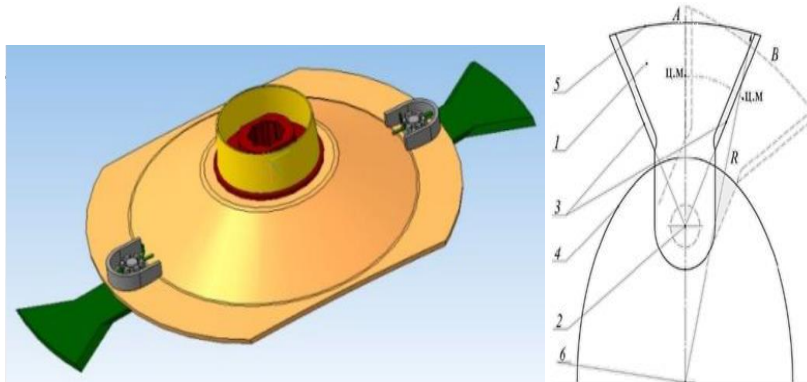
Конструкція трапецієподібного ножа роторної косарки:
